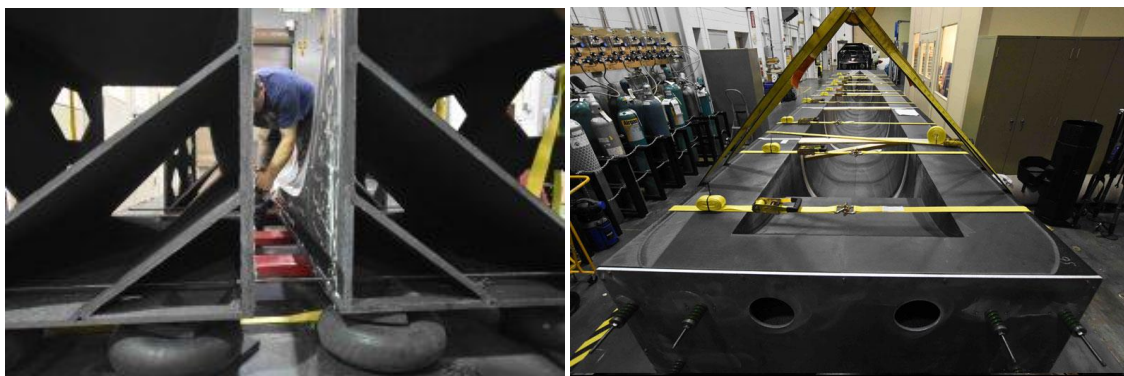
mecanizado de una de las secciones del molde del casco – Fuente: [proboat.com](http://proboat.com)
